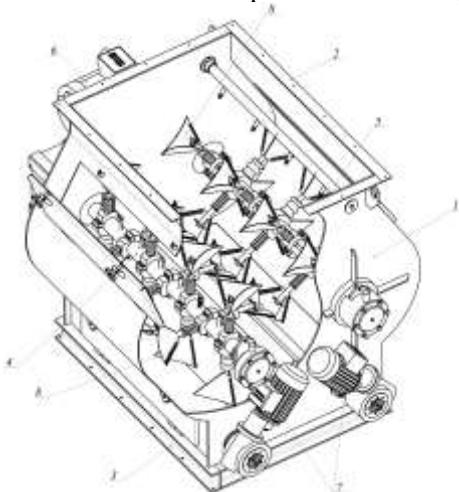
Двухвальный лопастной смеситель: 1 – ванна; 2 – загрузочный патрубкок; 3 – разгрузочный патрубкок; 4, 5 – валы; 6 – привод валов; 7 – привод выгрузных люков; 8 – лопасти
